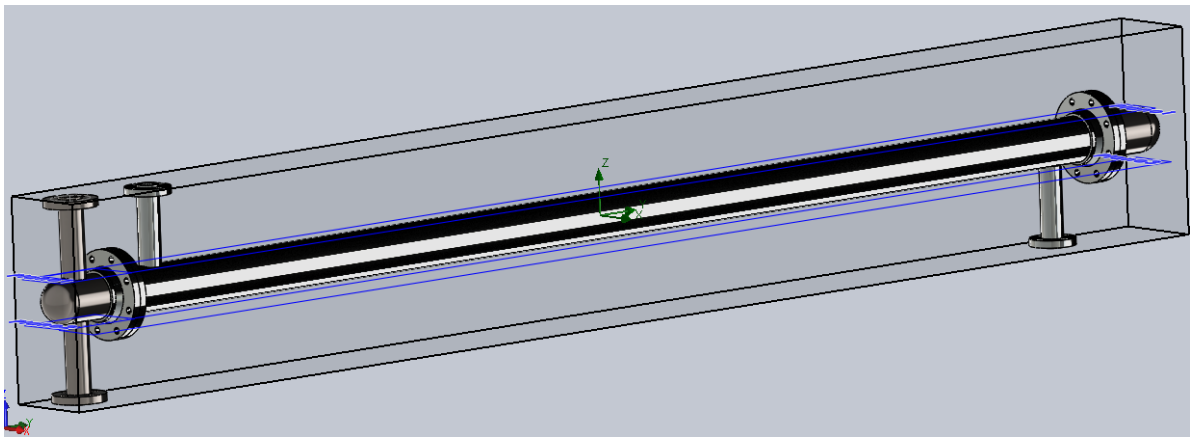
Vista detallada de la construcción del Intercambiador de calor de tubos y coraza para un sistema corrosivo. Fuente: SolidWorks
